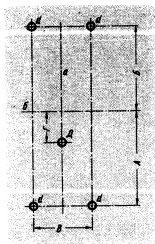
Сверление отверстий для установки на изоляционных плитах контакторов серии КП 500 с передним присоединением
